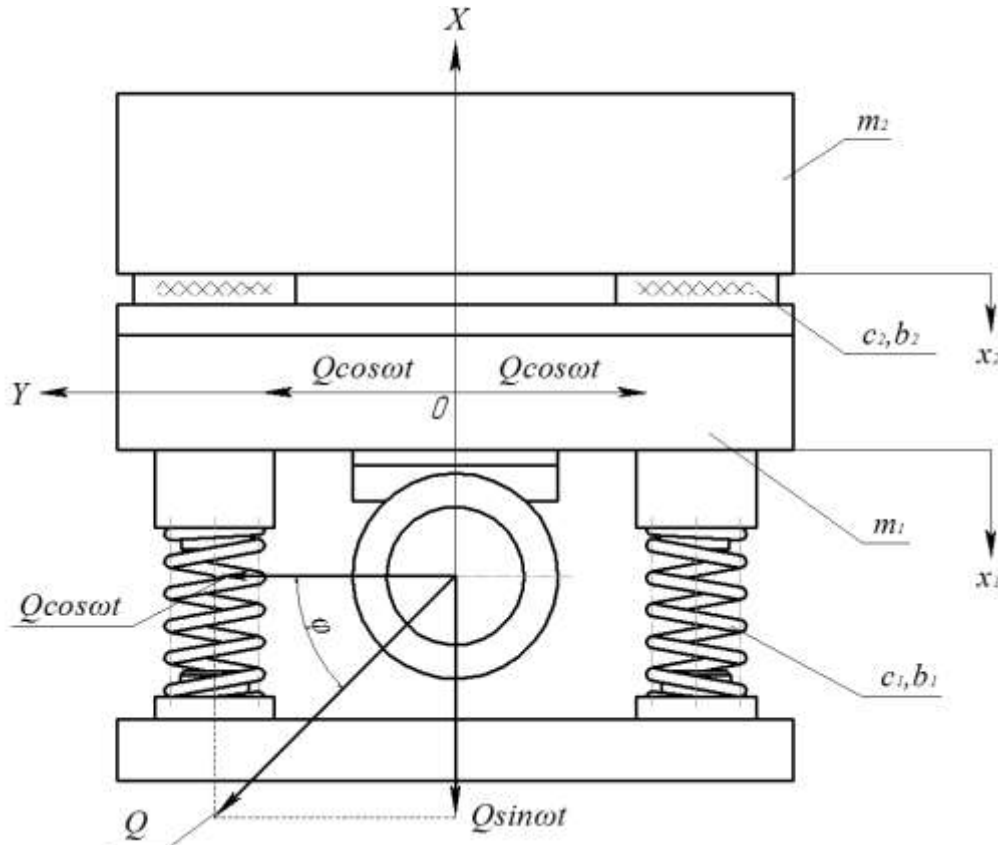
Расчетная схема двухмассной виброплощадки для формования бетонных изделий
